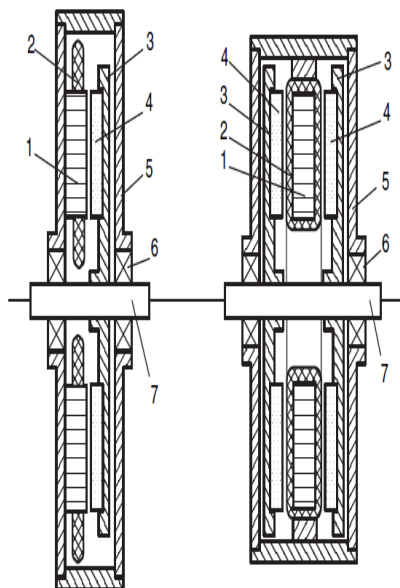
Загальний вигляд торцевого генератора із двосторонньою активною поверхнею: 1 – магнітне осердя статора; 2 – обмотка статора; 3 – ротор; 4 – постійні магніти; 5 – корпус; 6 – підшипники; 7 – вал.
